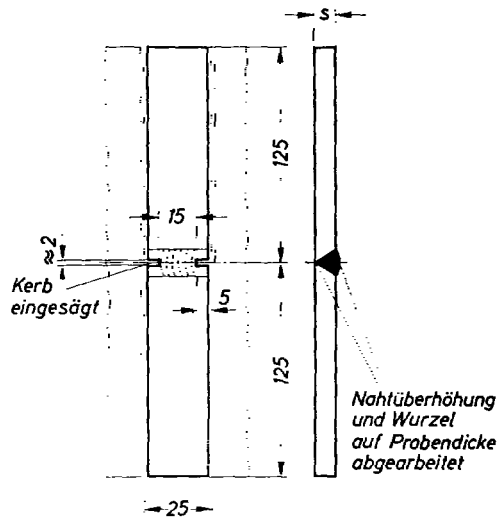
Kerbzugprobe Z_K und Kerbfaltprobe F_K für $s = 1,5$ bis 2 mm
